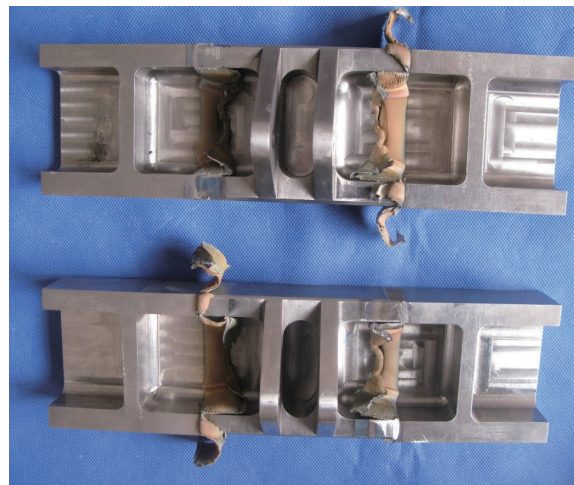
异种钛合金焊接的线性摩擦焊接头
